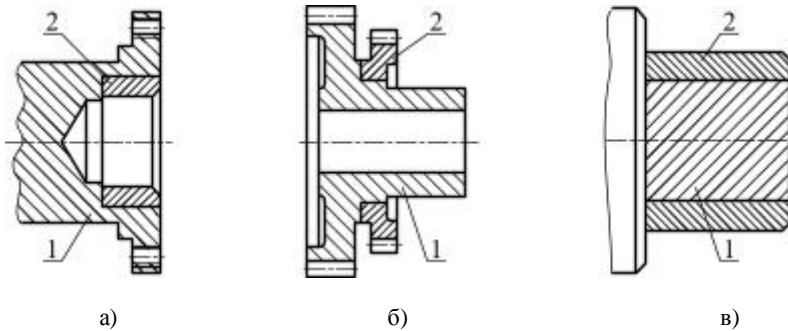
Відновлення спрацьованого отвору (а), шестерні (б) і шийки вала (в) способом заміни її частини: 1 – спрацьована деталь; 2 – додаткова деталь
